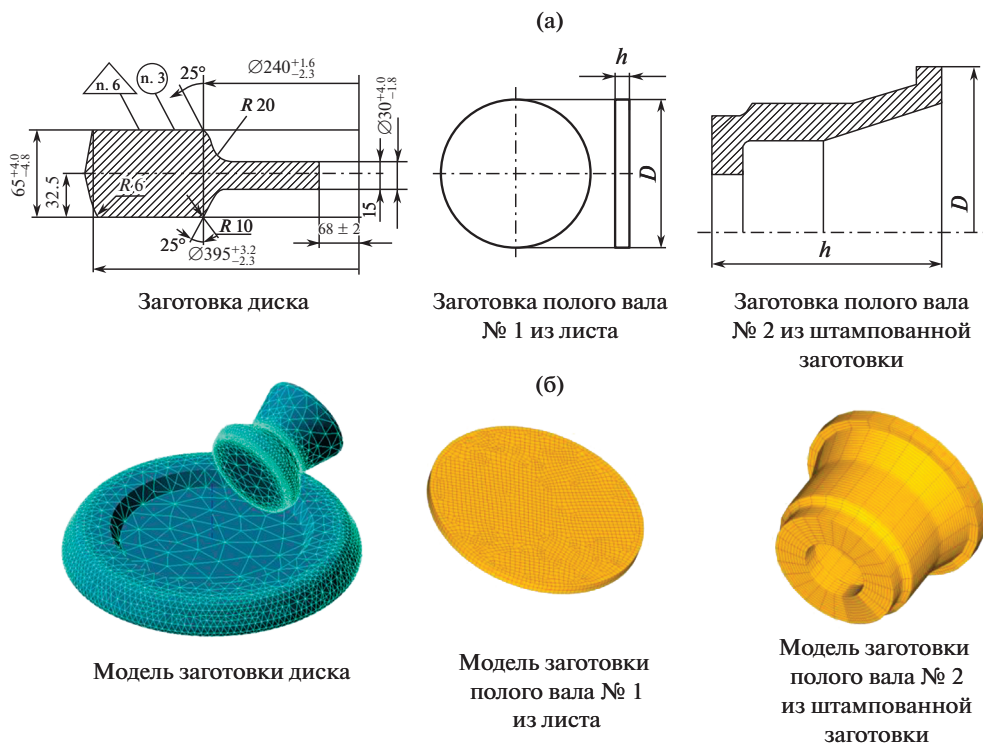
Исходные заготовки и конечноэлементные модели заготовок для раскатки полых валов: (а) — заготовки: диска, полого вала № 1 из листа, полого вала № 2 из штампованной заготовки; (б) — модели заготовок: диска (11200 конечных элементов); полого вала № 1 (4200 конечных элементов), полого вала № 2 (11760 конечных элементов).
